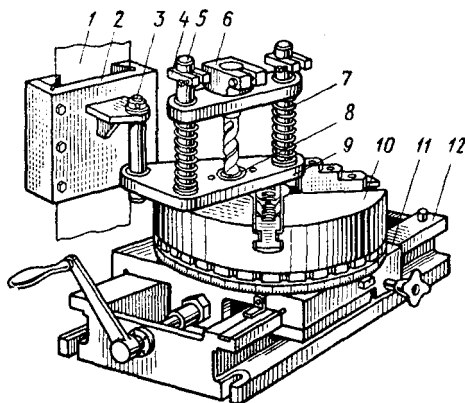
Универсально-наладочное приспособление к вертикально-сверлильным станкам
